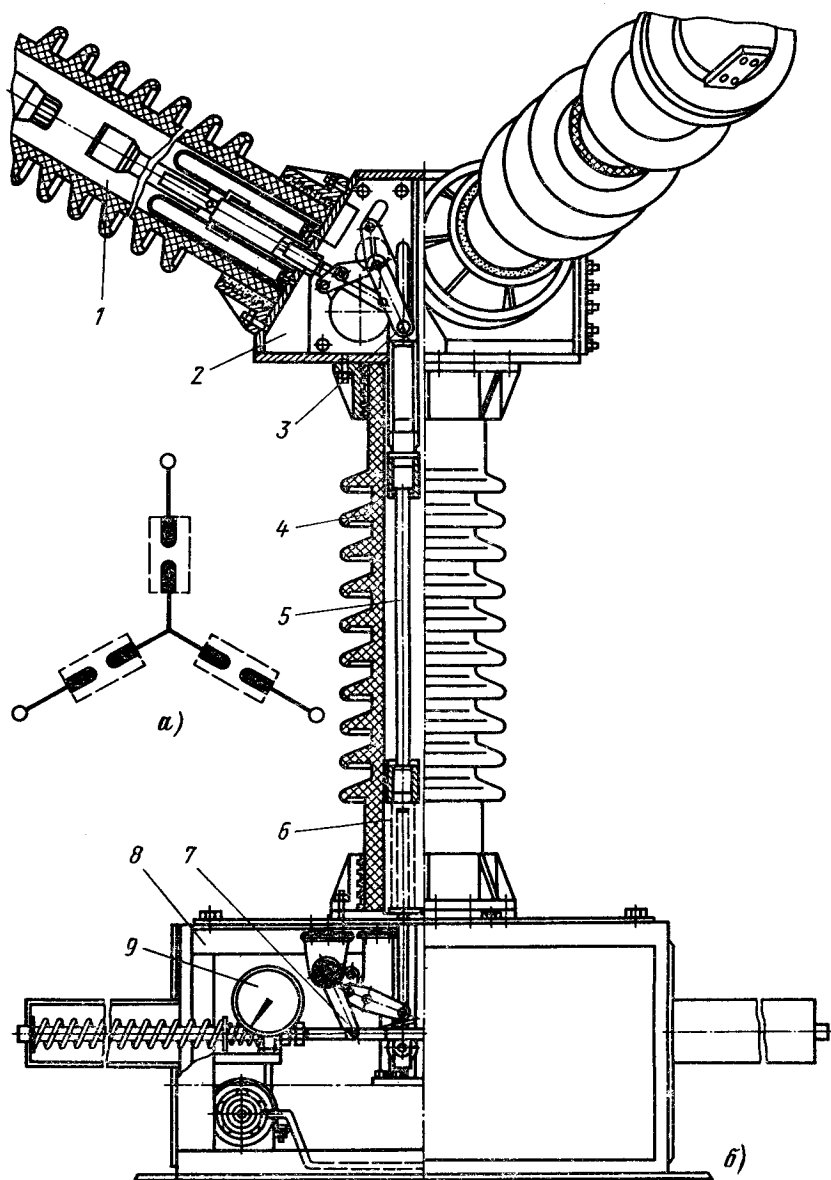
Выключатель нагрузки элегазовый на три направления.
